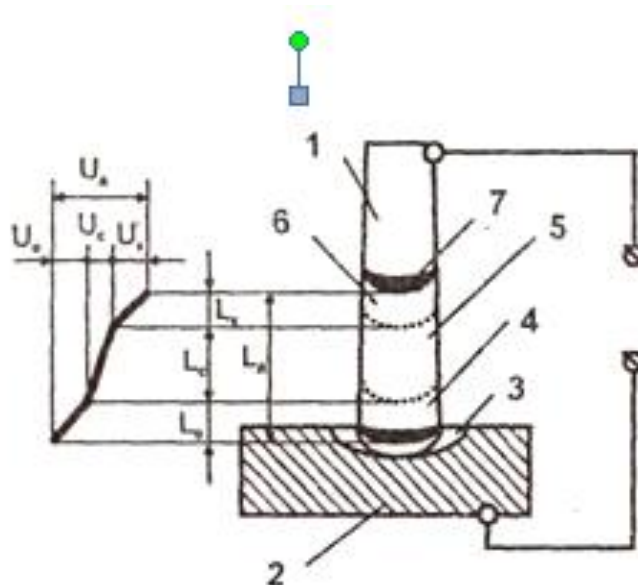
Схема сварочной дуги и падения напряжений в ней:
